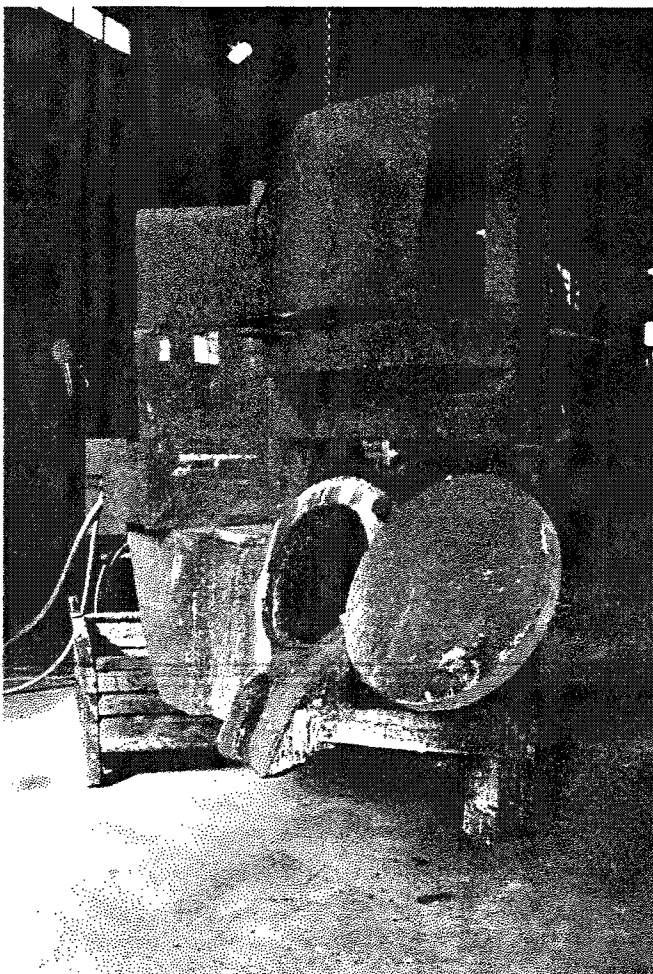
A/B: Postazione schermata di colata sollevata dal pavimento essendo appesa su monorotaia
